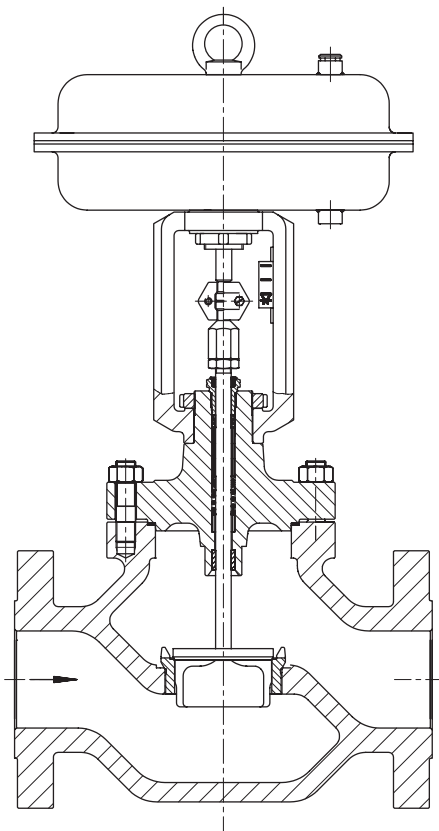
· Регулирующий клапан типа 3251-1 с пневматическим приводом типа 3271
